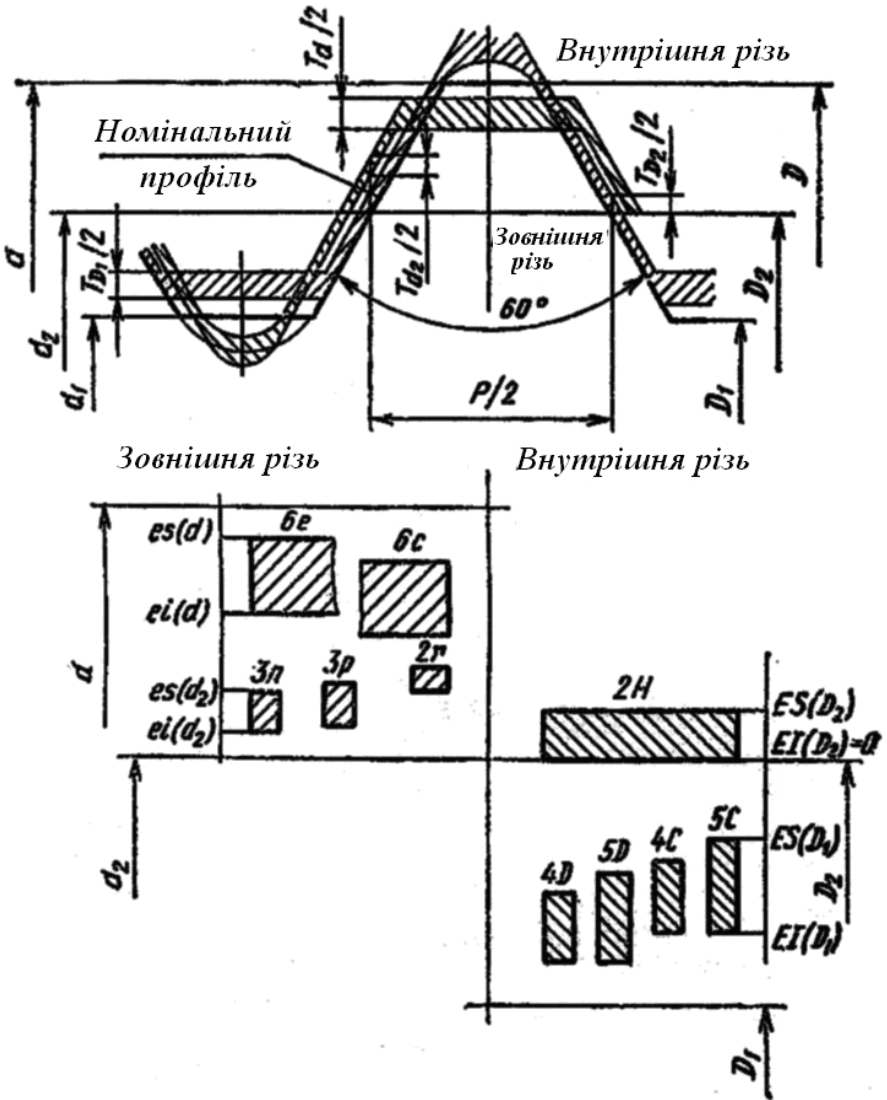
Розташування полів допусків різі з натягом
